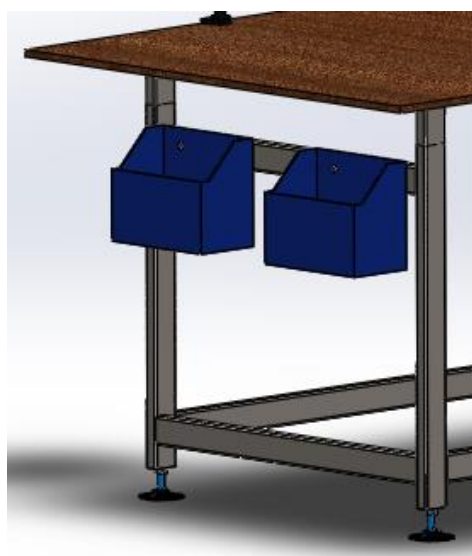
Caixes d'eines a les taules de treball. Font pròpia
